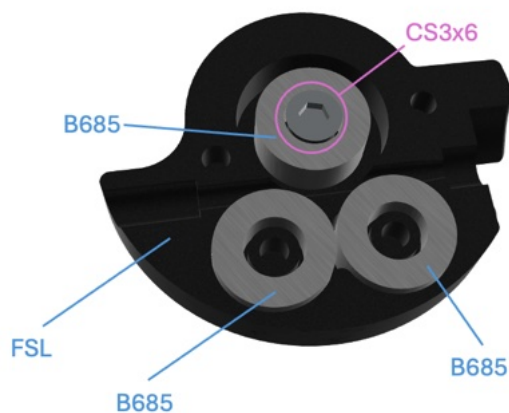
Rewinder-Chassis Montageschritt 14.
